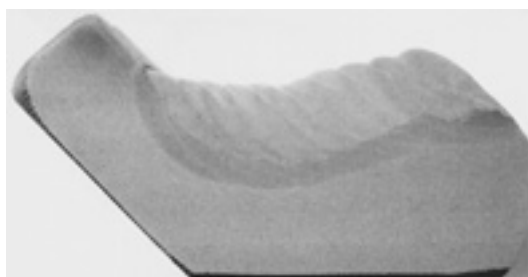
Макроструктура металла гребня вагонного колеса, наплавленного проволокой Св-08ХГ2СМФ под флюсом ФКН-7
